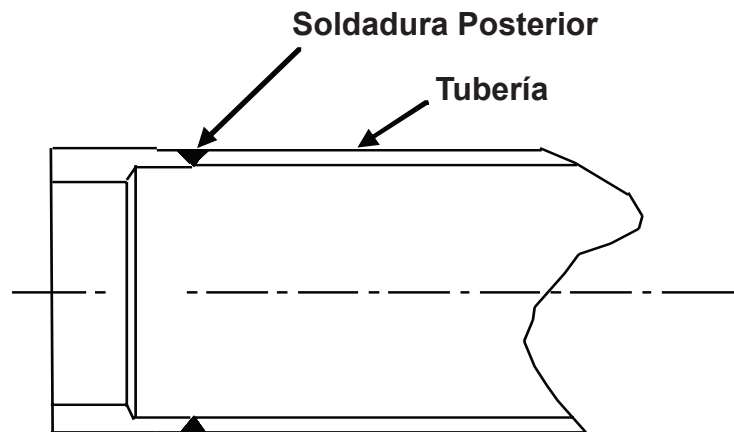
Tipo Asentada al Exterior de la Zapata con Soldadura Trasera
